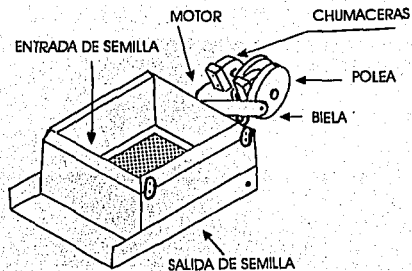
DESCRIPCIÓN DEL ELEMENTO MECÁNICO
